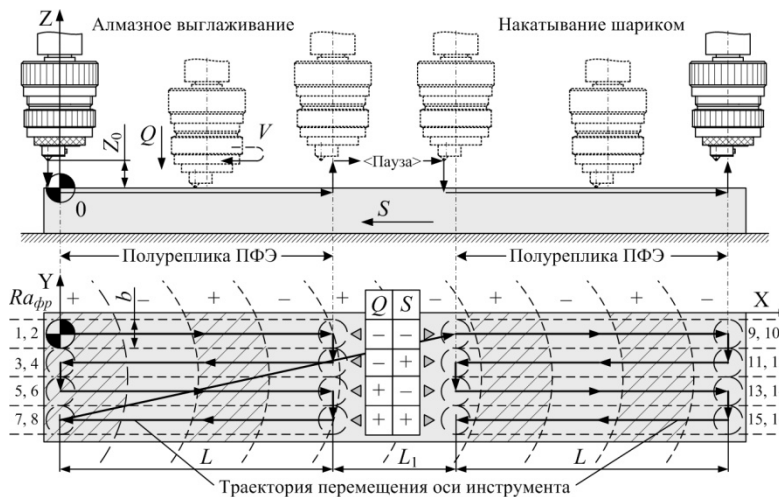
Схема обработки плоской поверхности заготовки методами ПFD при реализации полуребрик плана ПФЭ в процессе ЭДТС на станке с ЧПУ
